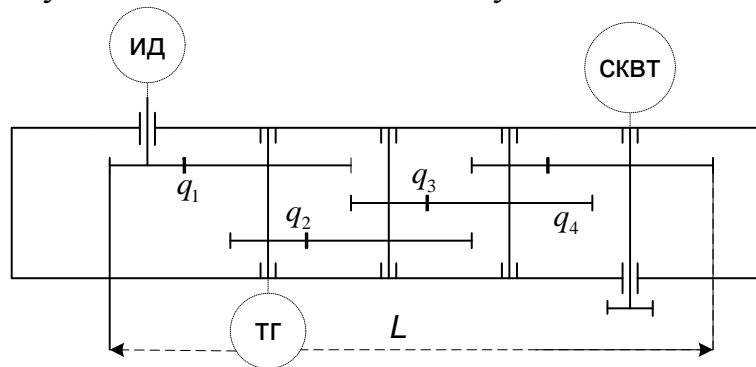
Кинематическая схема четырехпарного редуктора с одинаковыми передаточными отношениями пар.
